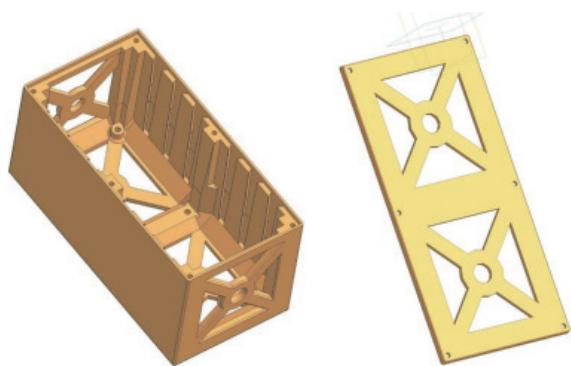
Подготовка управляющего кода для печати корпуса МКА НК в САМ модуле
